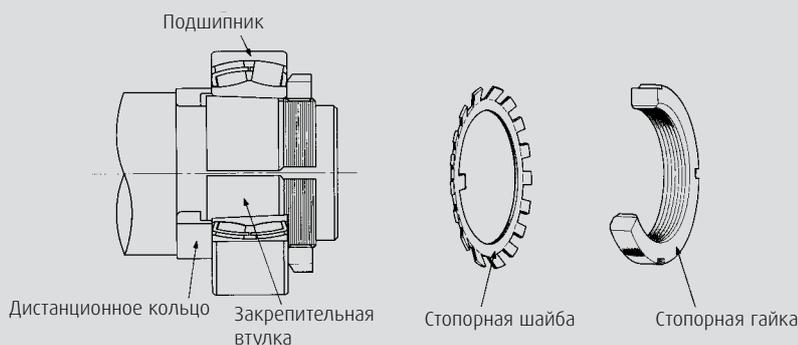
Установка стопорной шайбы по окончании регулировки зазора
